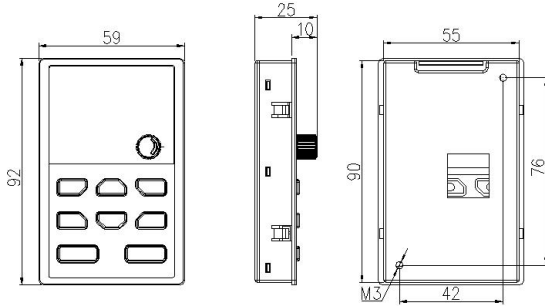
键盘安装开孔尺寸 55*90 (mm)
